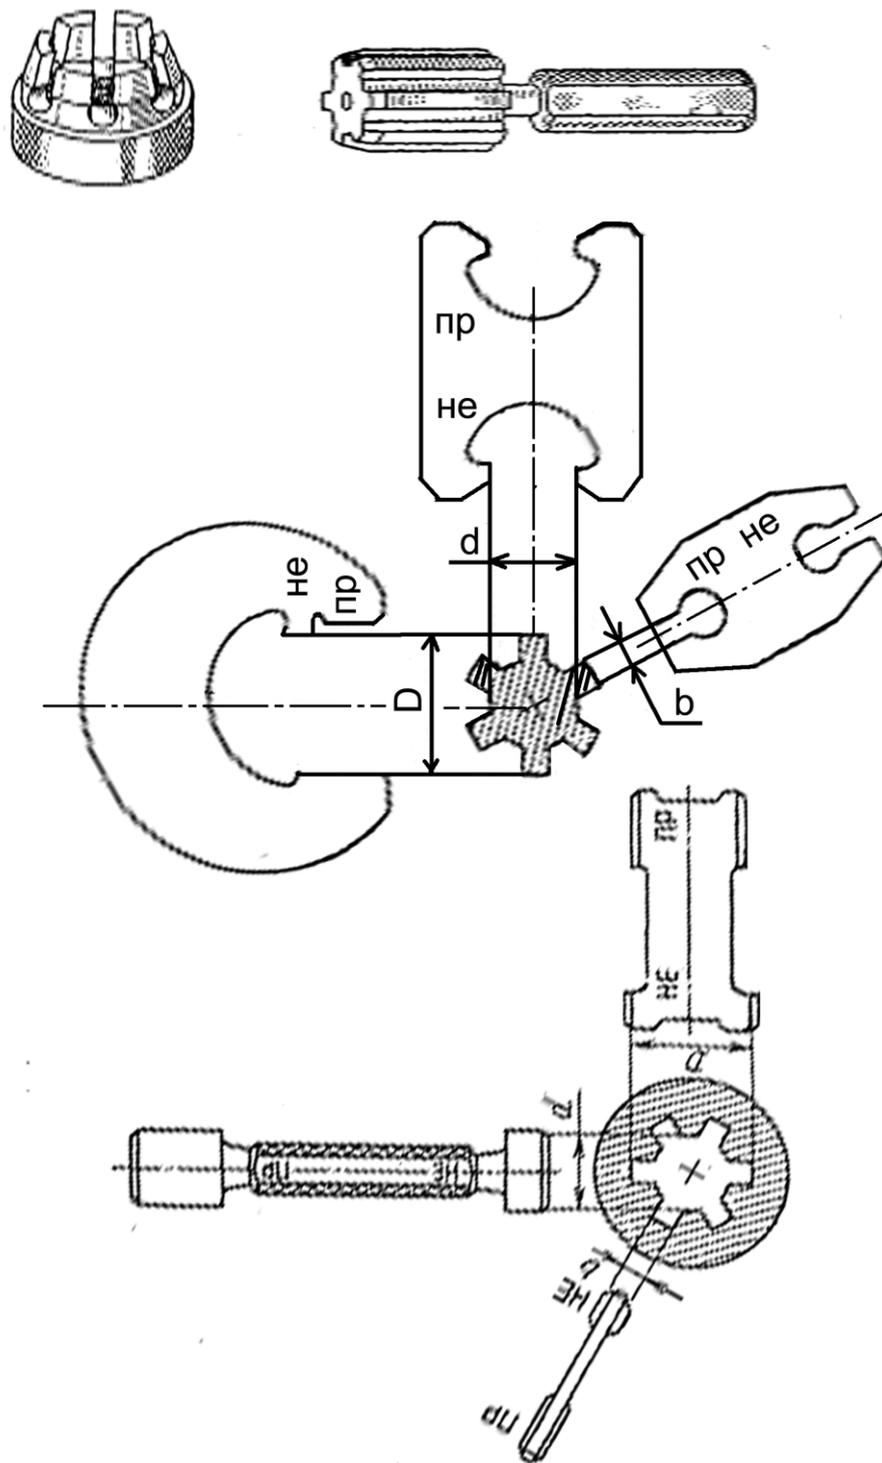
Полный комплект калибров для контроля прямобочного шлицевого вала и отверстия.
